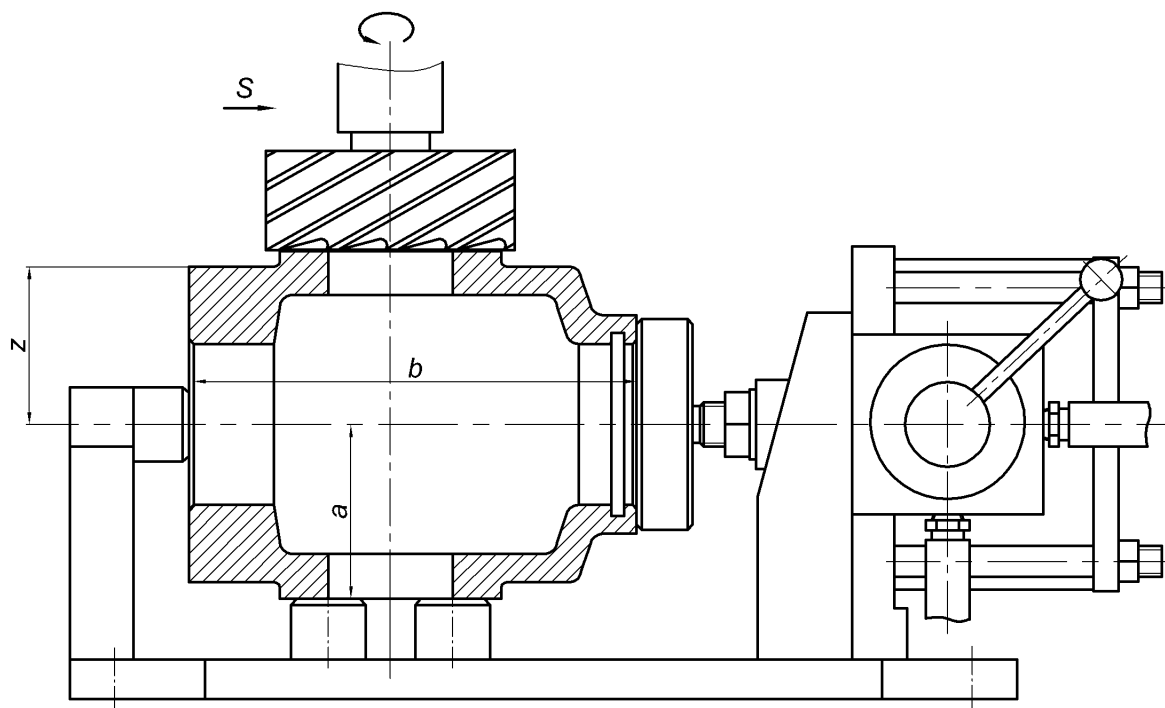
Схема встановлення заготовки у пристосуванні для фрезерування площин
